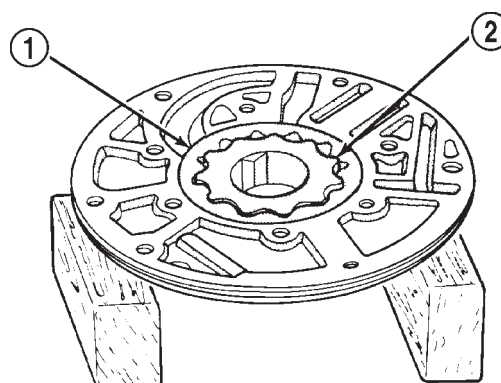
Apoyo de la bomba e instalación del engranaje exterior
